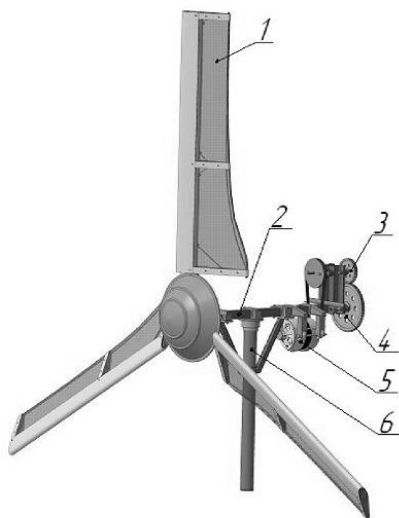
Основные узлы установки: 1-ветровое колесо; 2-несущая рама; 3-верхний подшипниковый узел; 4-нижний подшипниковый узел; 5-генераторная установка, 6-опорно-поворотный узел
